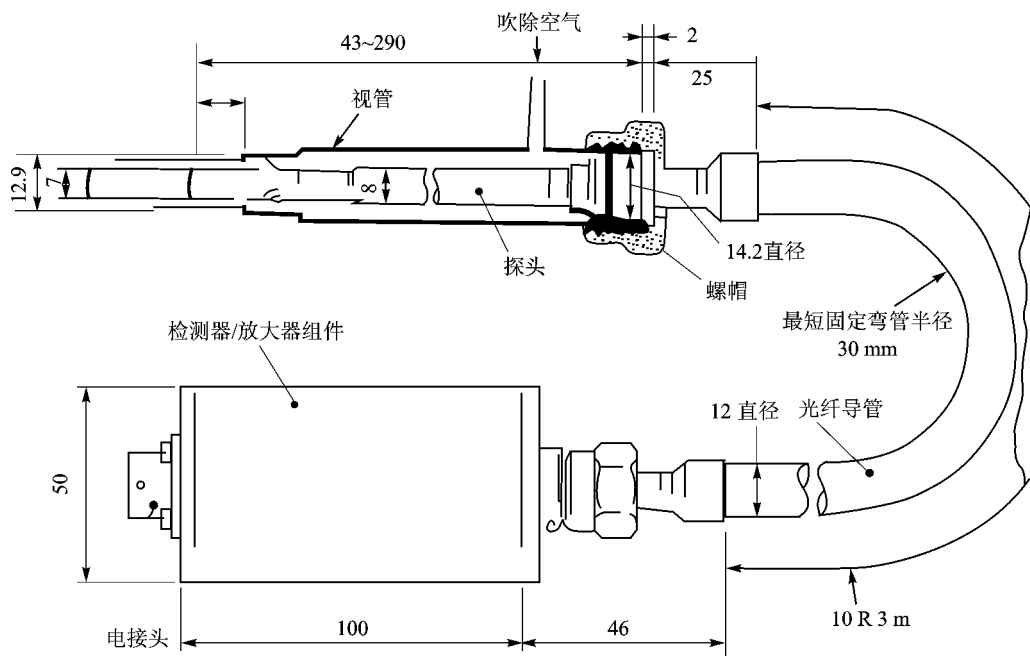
涡轮温度传感器外形示意图及几何尺寸
